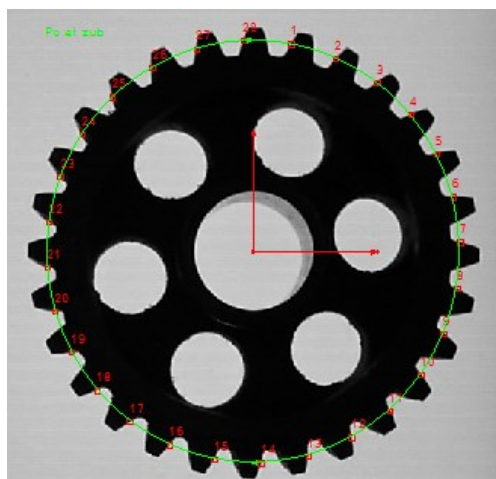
Nastavení kroku detekce ozubeného kola 1
